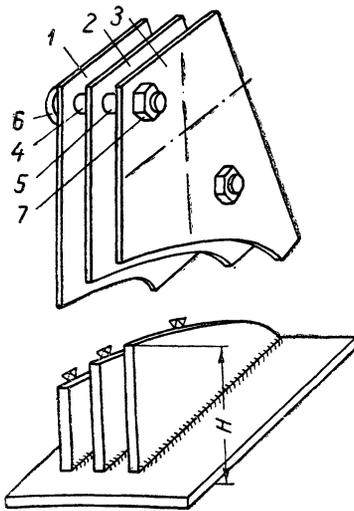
Разметка сварных узлов приспособлений.
